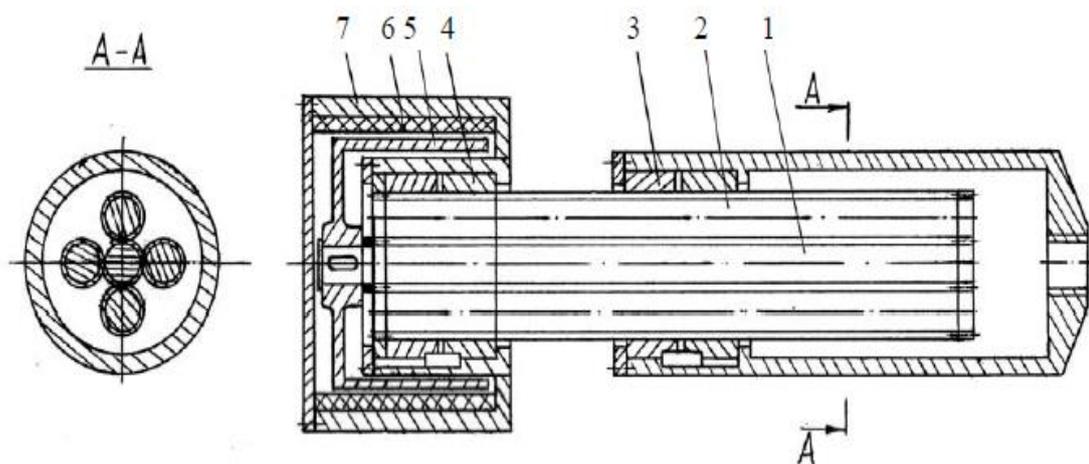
Электропривод с передачей с длинными резьбовыми роликами
